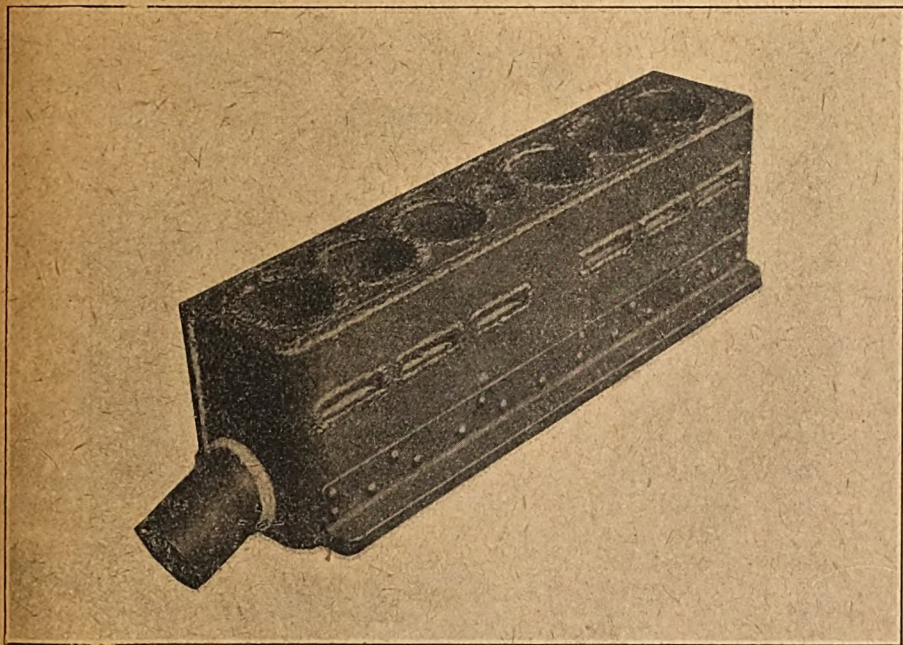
Bloc moteur Voisin en acier, entièrement soudé à l'arc.
